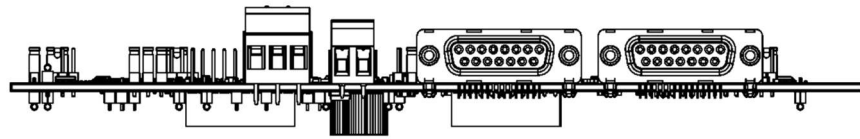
BP-AM2BLDCSERVO PCB 模组 - 底视图
